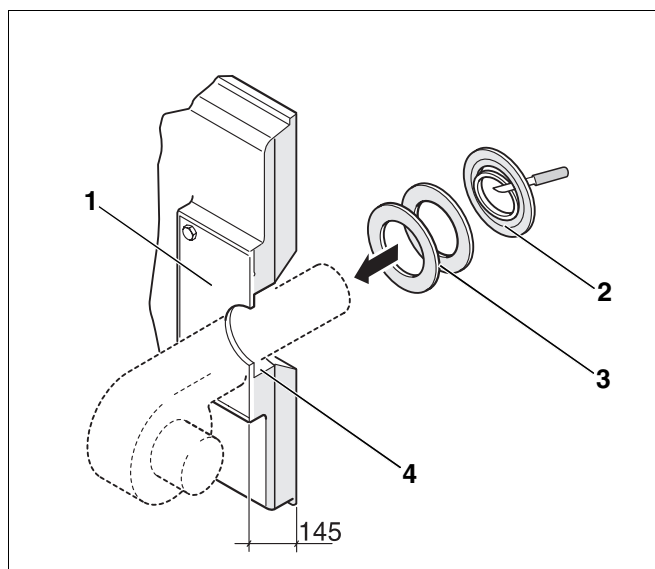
Montarea arzătorului (dimensiunea în mm)
